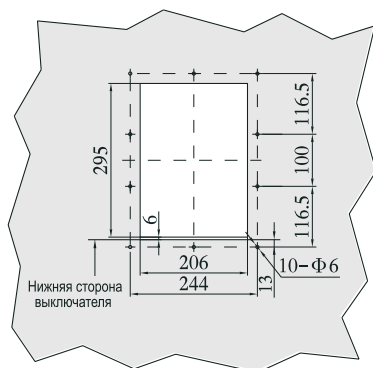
Габаритные размеры стационарных трехполюсных выключателей типоразмера F
